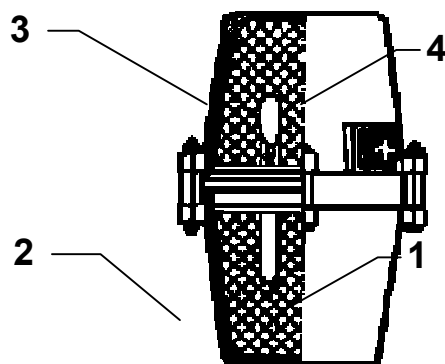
Конструкция генератора с оппозиционным расположением зарядов: 1 – корпус; 2 – аэрозолеобразующий заряд; 3 – узел запуска; 4 – клеммная колодка
